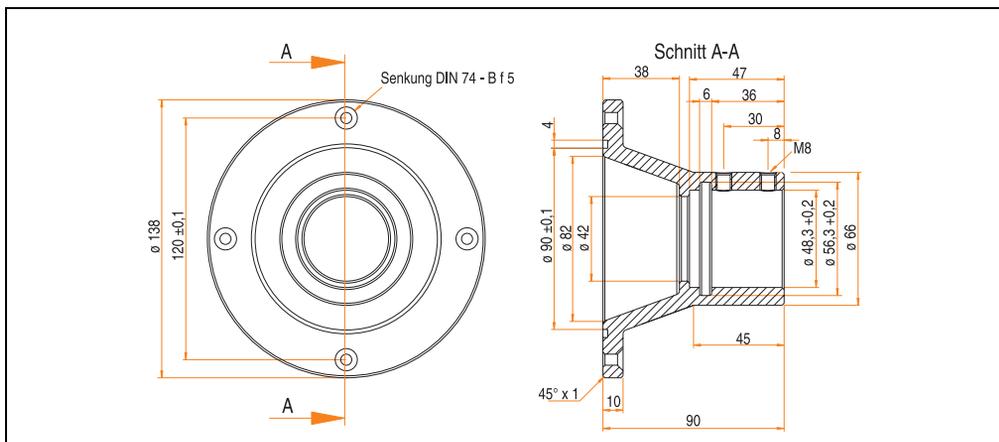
Abmessungen Panel Flansch Adapter 5A5007.01
